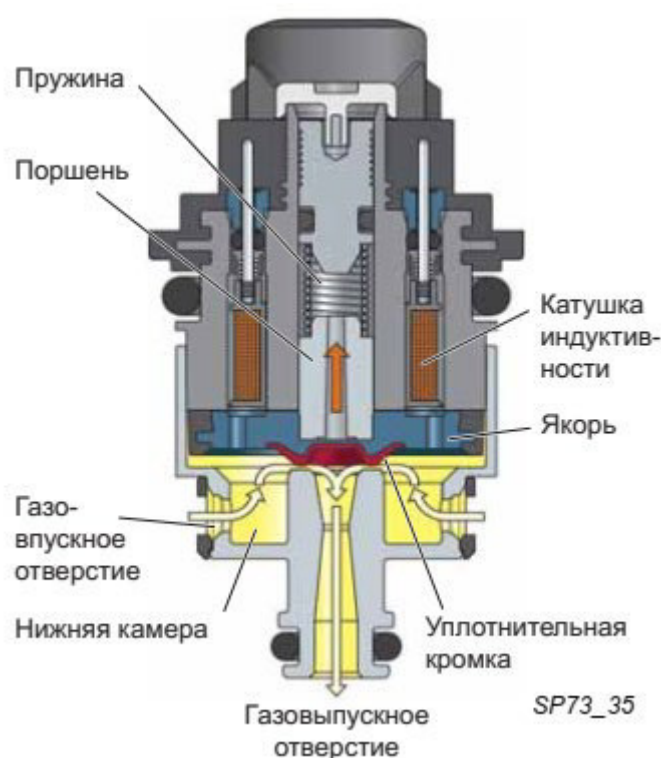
Схема роботи газової форсунки (відкритий стан)
